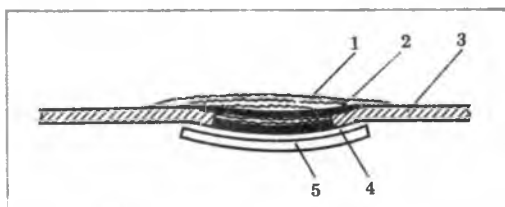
Накладка заплатки из стеклоткани на поврежденную панель, насаженную вовнутрь: 1 — стеклоткань; 2 — смола; 3 — панель; 4 — разделительный слой; 5 — твердая подкладка внутренней стороны
